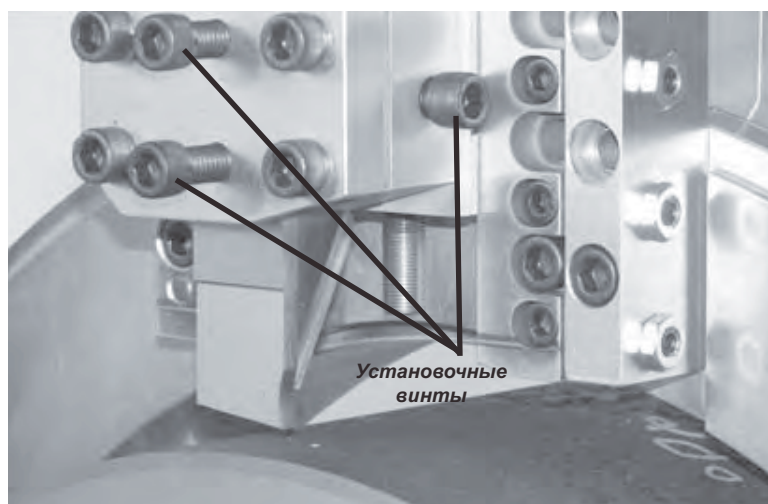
Для установки резцов для снятия фаски следует использовать три установочных винта.
